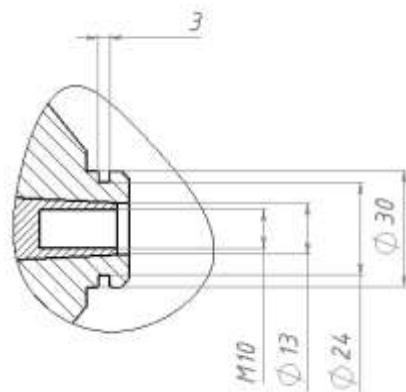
Конструктивные размеры соединения крыльчатки вентилятора с осью электродвигателя
